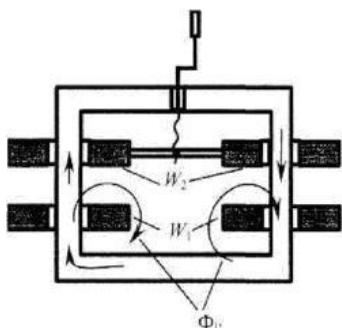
Устройство сварочного трансформатора с подвижными обмотками: при полностью сдвинутых обмотках сварочный ток максимальный, при раздвинутых - минимальный.
